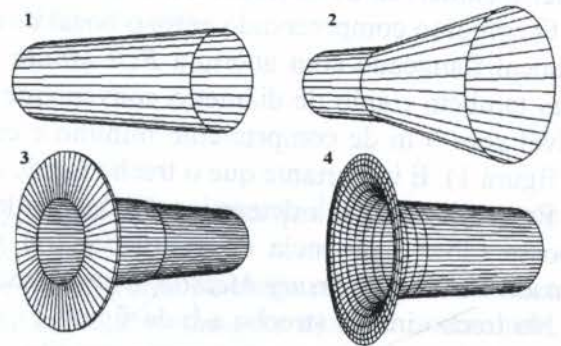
Tipos de bocal.: 1. simples, sem flange; 2. flange cônica; 3. flange reta; 4. bell mouth
